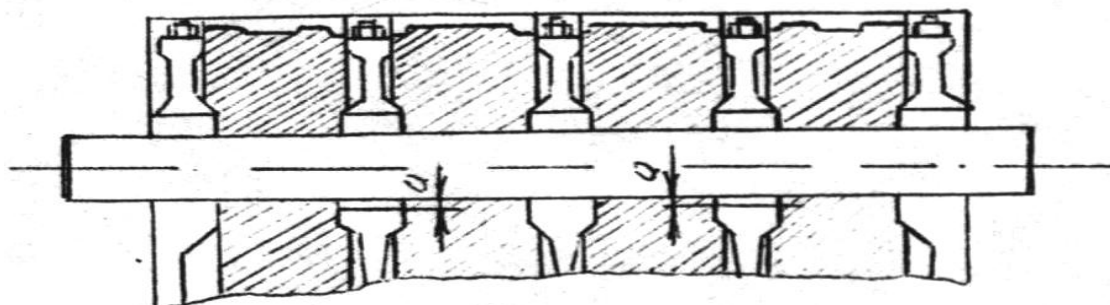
Схема контроля соосности гнезд блока цилиндров под вкладыши коренных подшипников с помощью оправки.
